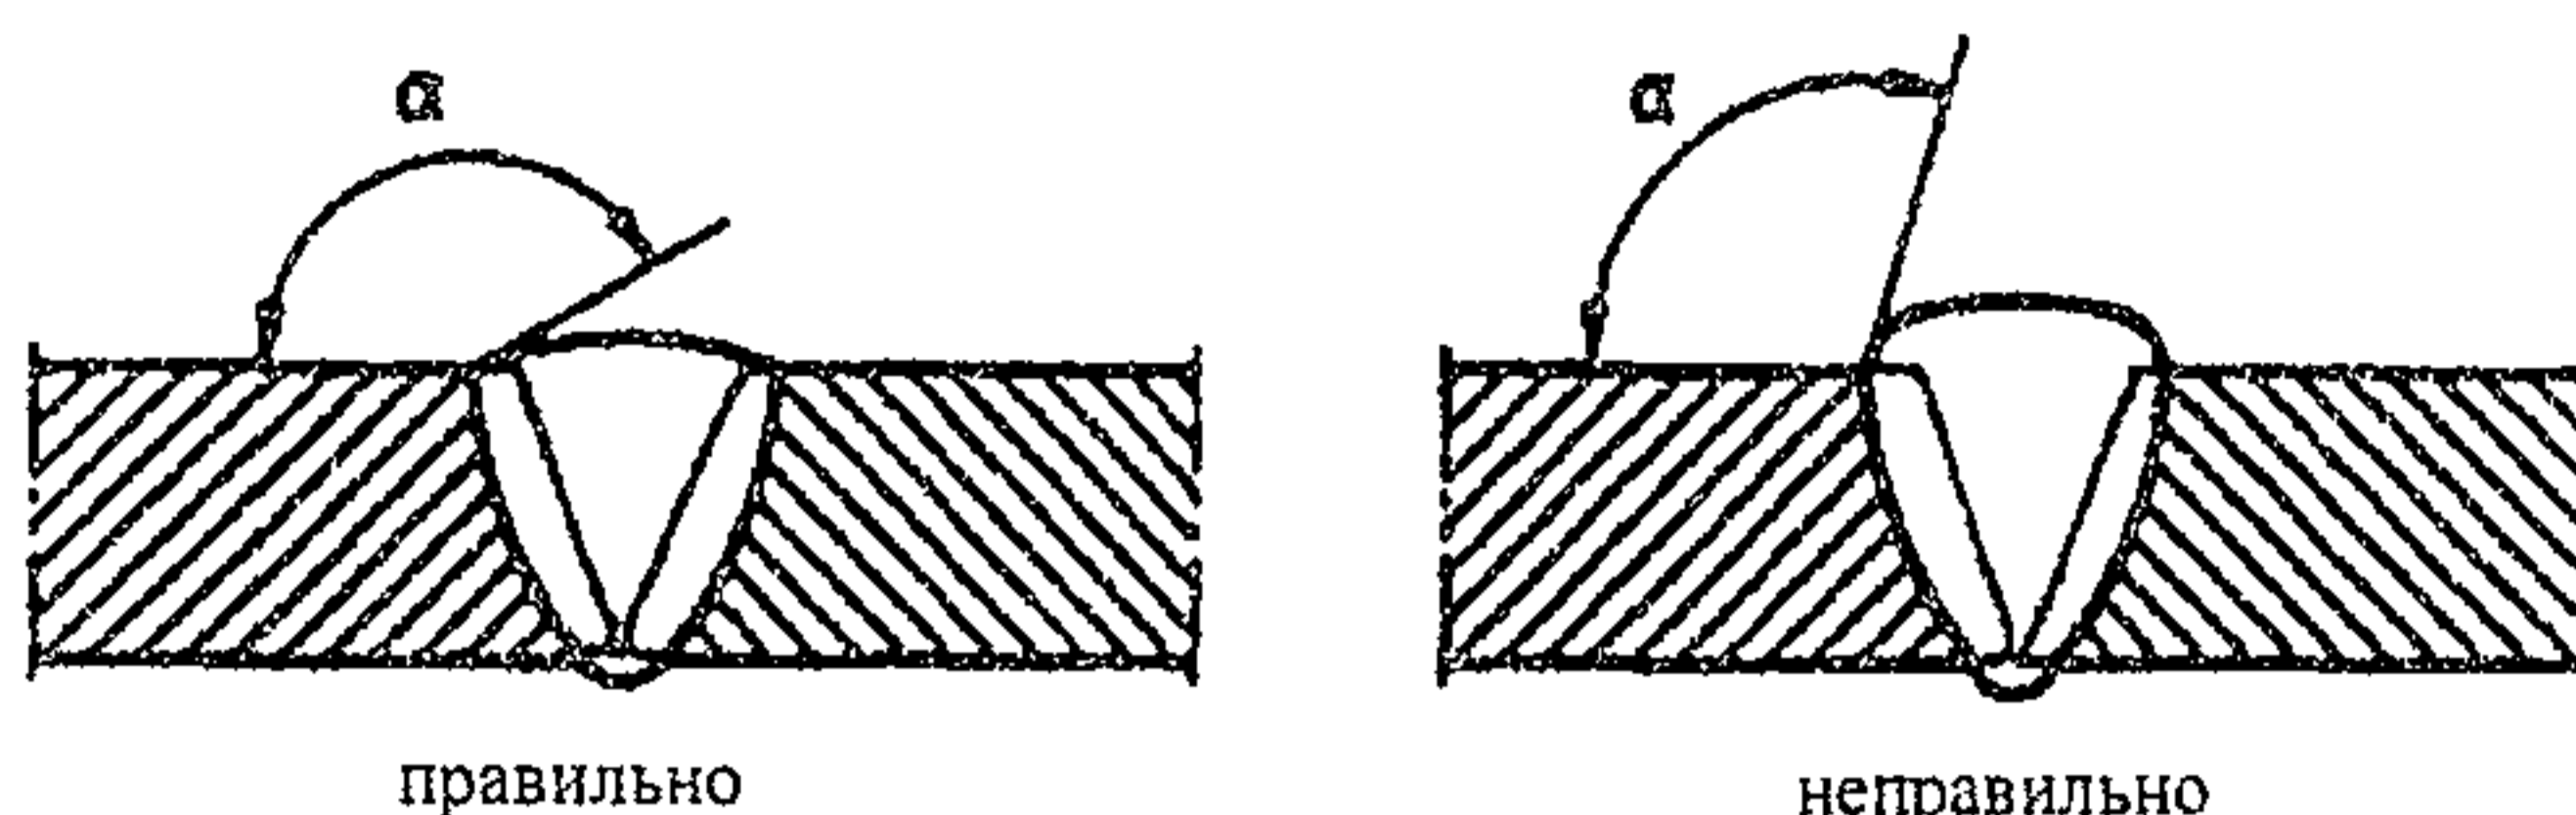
Неправильный профиль сварного шва
